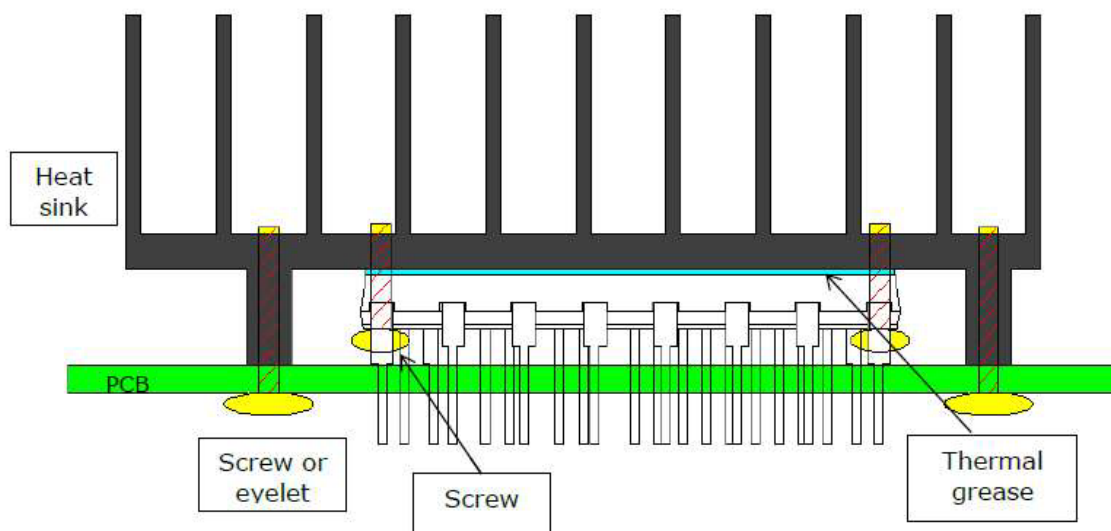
Recomendación de unión radiador-IPM-PCB. Fuente: InfineON
